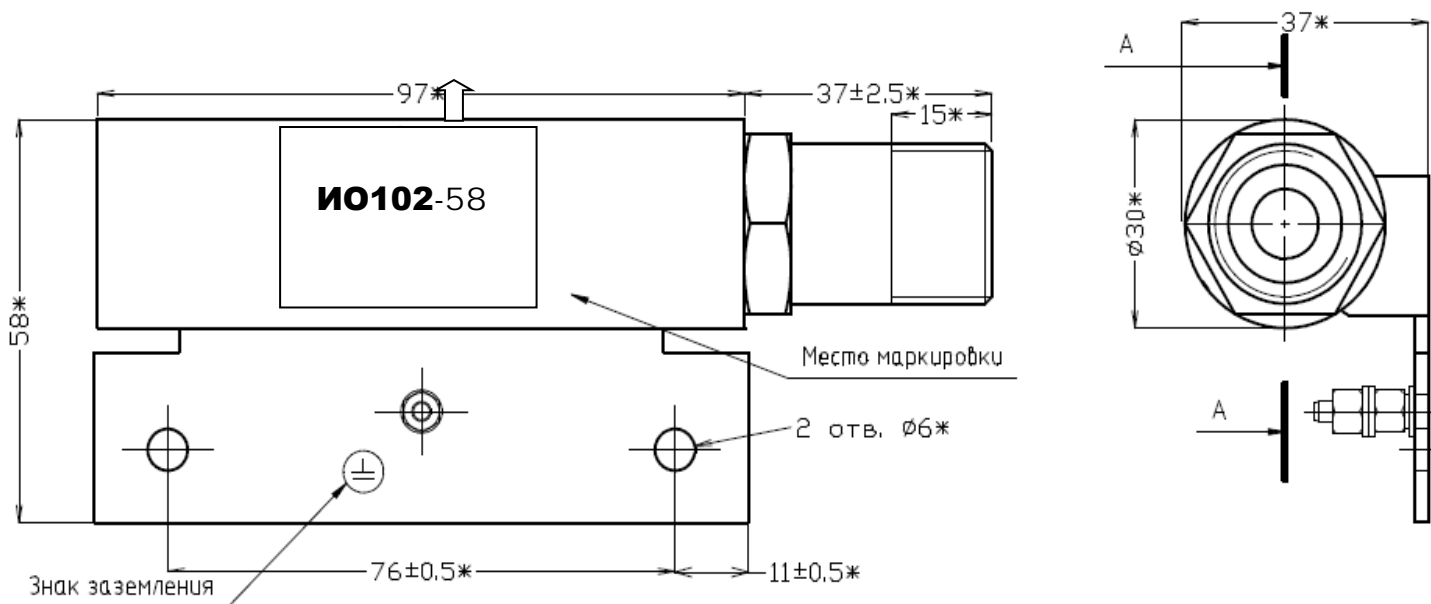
Габаритные и установочные размеры исполнительного блока ИО102-58
